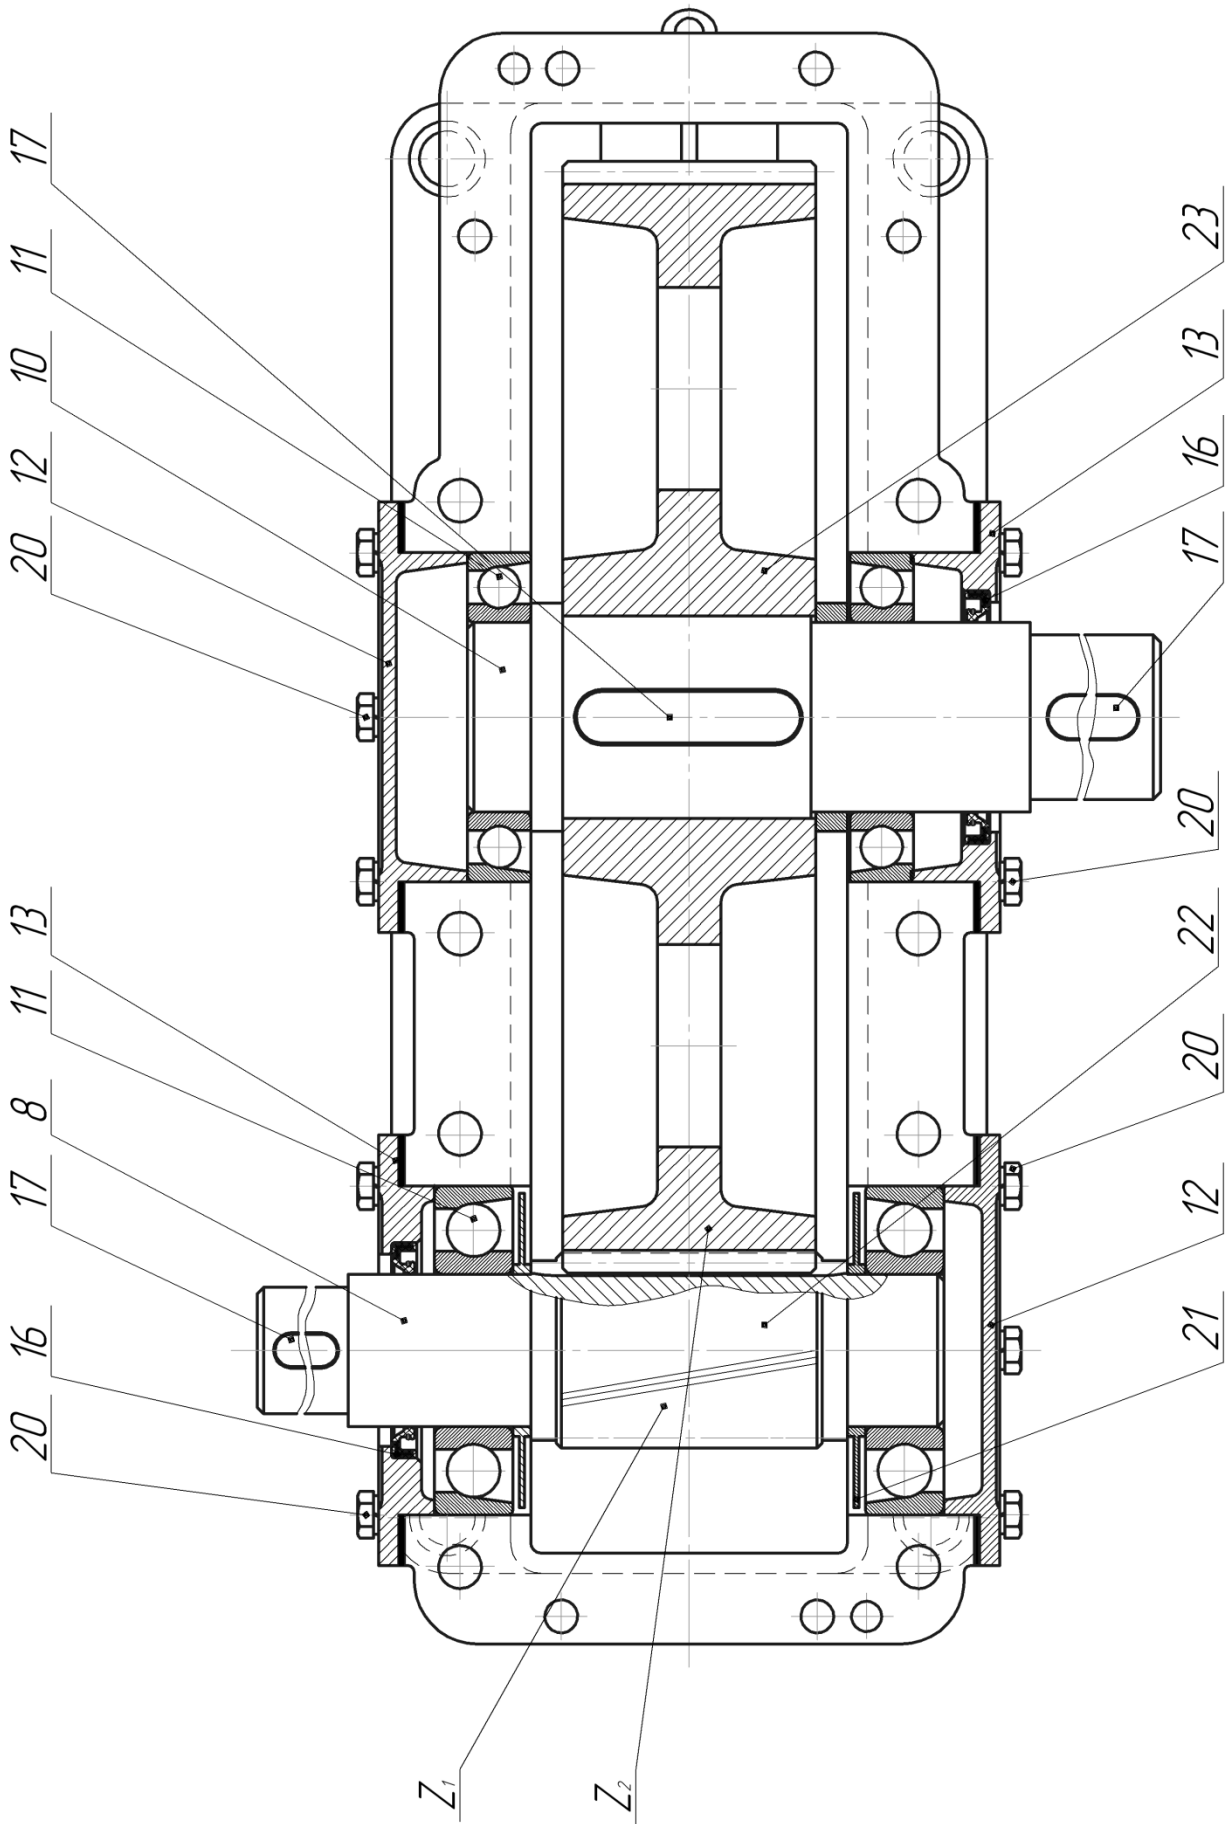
| Конструкция одноступенчатого цилиндрического редуктора (вид сверху)
